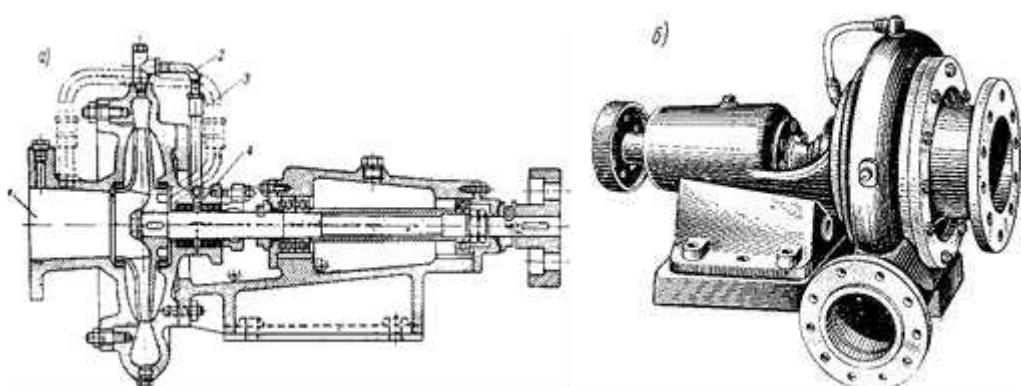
Одноступенчатый центробежный насос [5]
